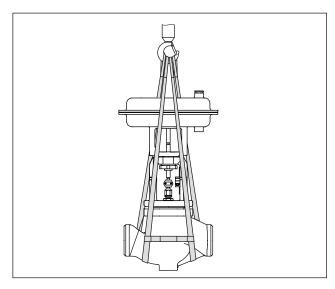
Подъем регулирующего клапана с патрубками под приварку (примерное изображение): подъёмные петли, размещённые на корпусе, должны быть скреплены друг с другом с помощью соединительного устройства, чтобы предотвратить их соскальзывание.
